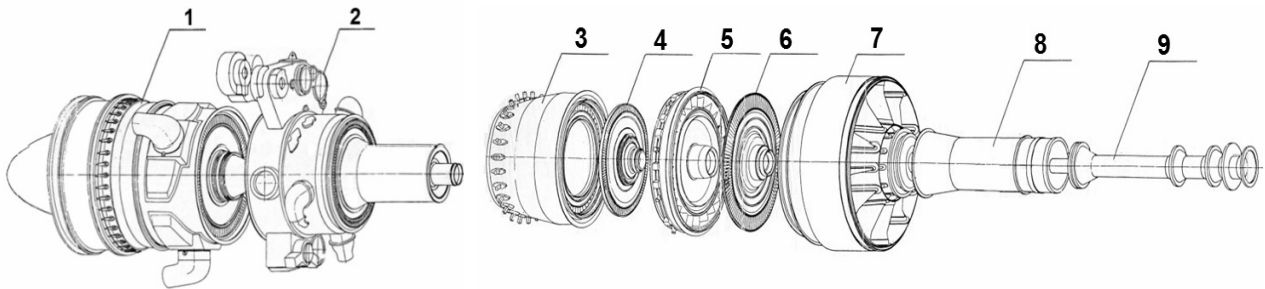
Компоновочная схема двигателя модульной конструкции типа Д-336:
